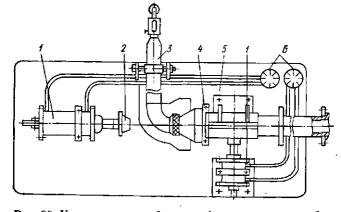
Установка для отбортовки фторопластовых труб с нагревом:
